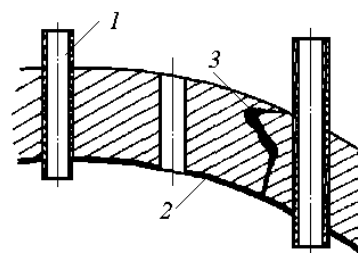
Фрагмент крышки корпуса реактора: 1 - патрубков ввода органа СУЗ; 2 - наплавка из нержавеющей стали; 3 – обнаруженная трещина.
